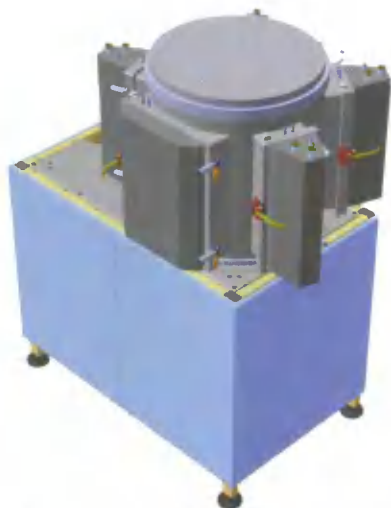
Конструкторская модель установки «Каролина Д-12Б» с закрытыми дверями.
